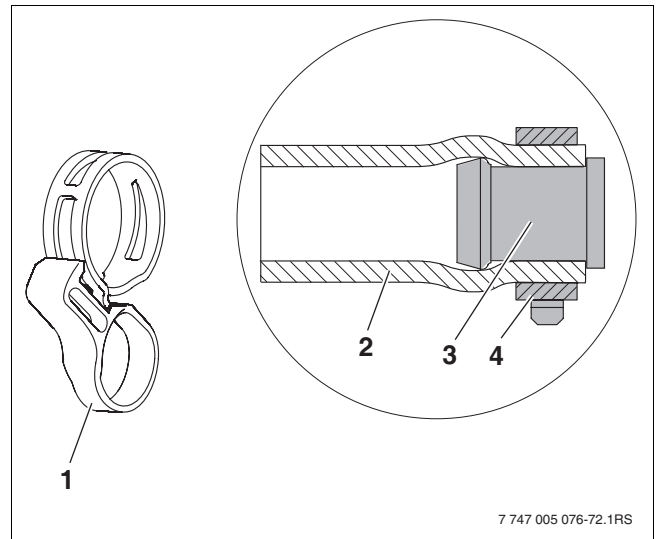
Abraçadeira de mola com anel de retenção e no estado montado no tampão cego pré-montado.
